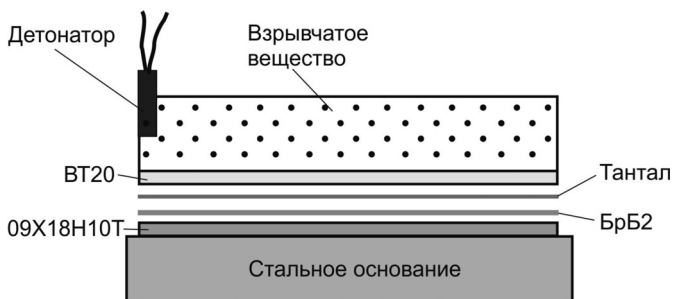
Схема сварки взрывом четырехслойного композита
